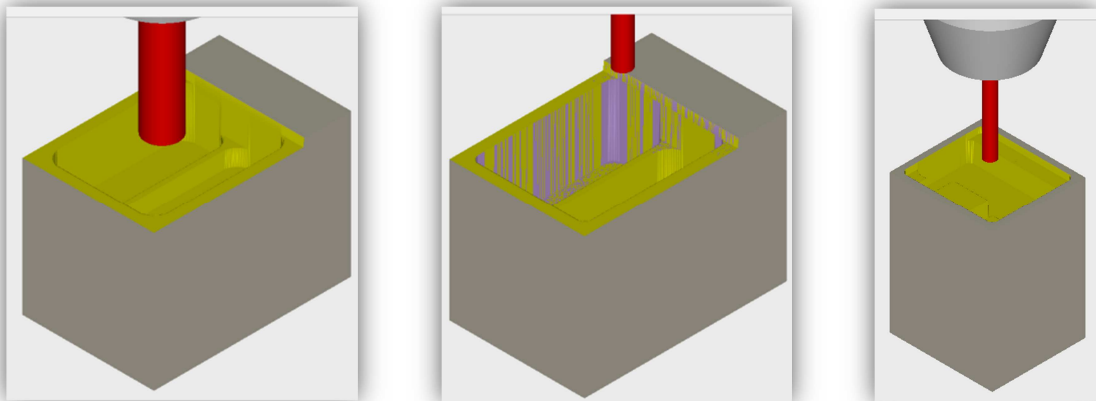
Proceso de maquinado de la carcasa del calibrador (Fuente: Propia).
